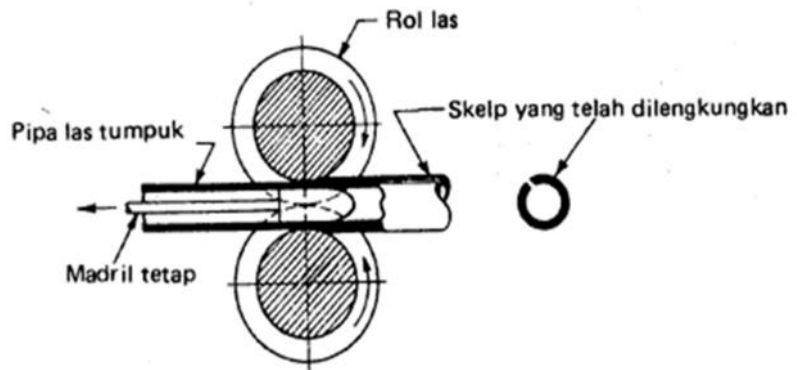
Susunan rol pada proses pengerolan pipa las lantak
